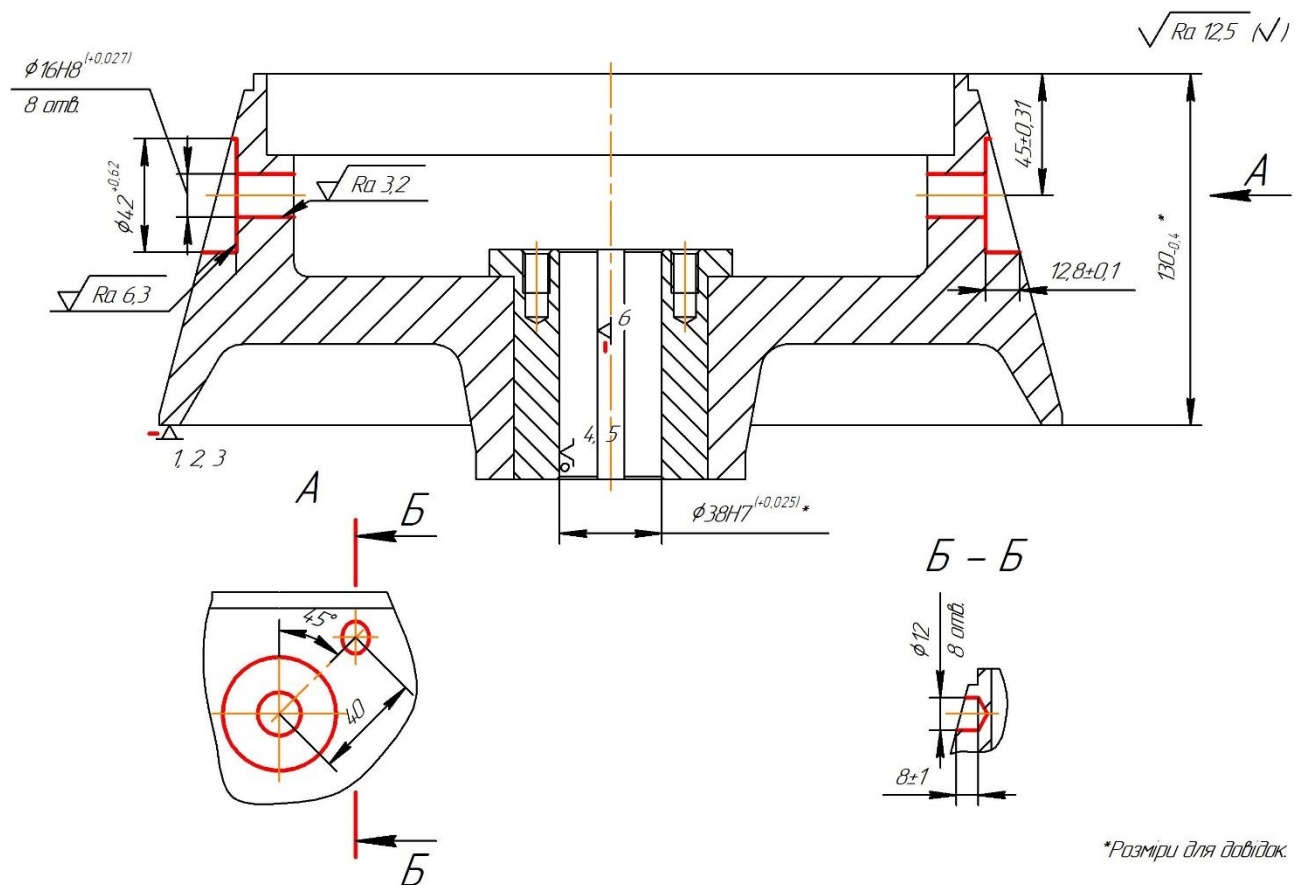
Альтернативна схема базування заготовки на операції 065
